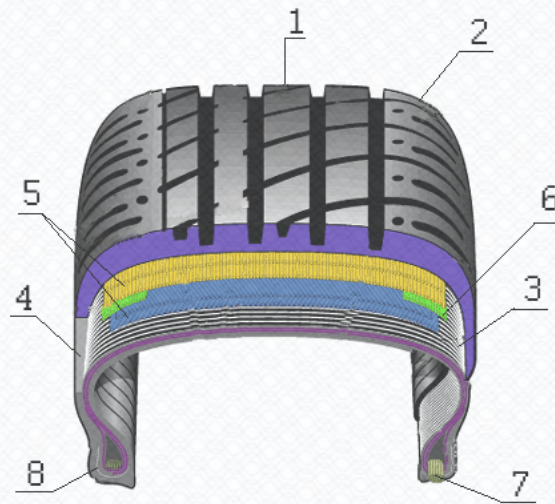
Конструкція сучасної пневматичної шини: 1 — протектор зрізними кільцями рисунку; 2 — плечовий блок з ламелями; 3 — каркас; 4 — боковина; 5 і 6 —шари брекера; 7 — бортове кільце; 8 — борт шини
